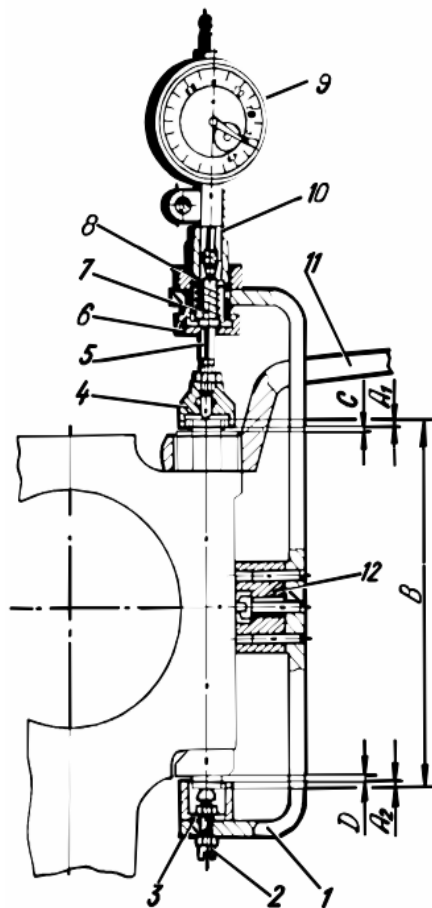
Приспособление для замера удлинения шатунных болтов при затяжке:
